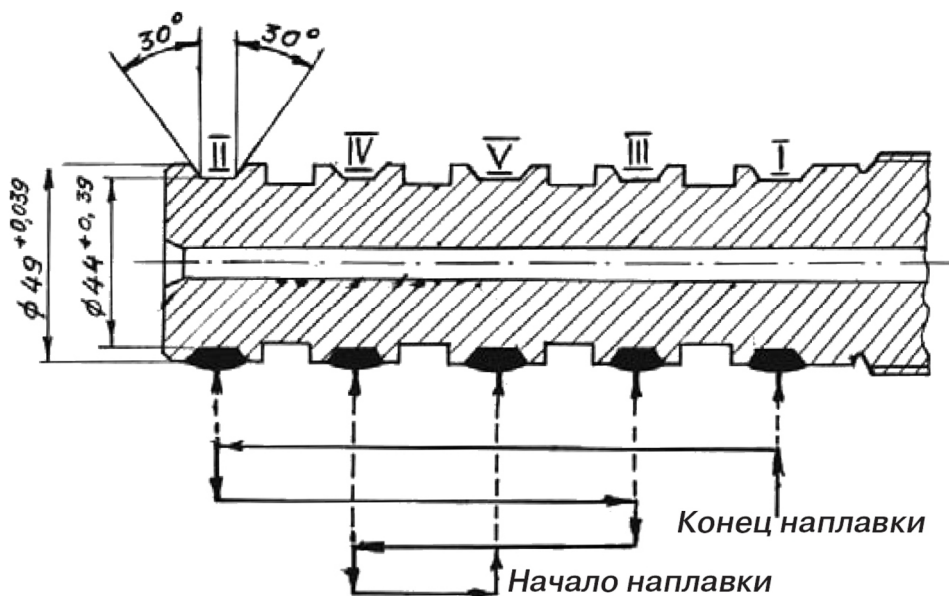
Схема подготовки и наплавки канавок вторичного вала 150.37.037-2 коробки передач
